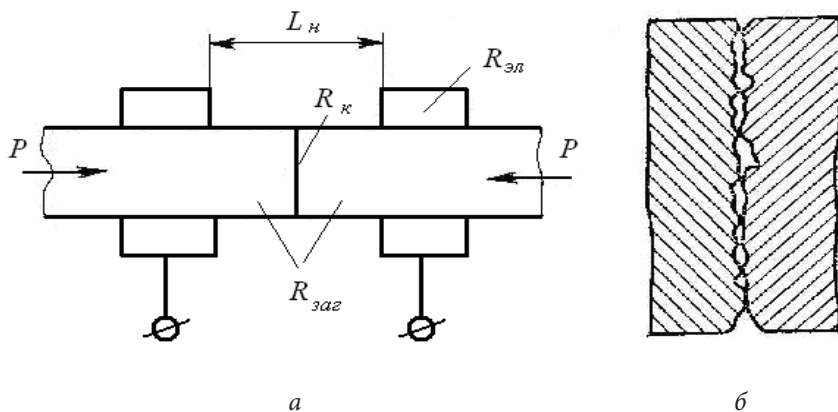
Схема контактной сварки (а) и физического контакта (б) свариваемых деталей
